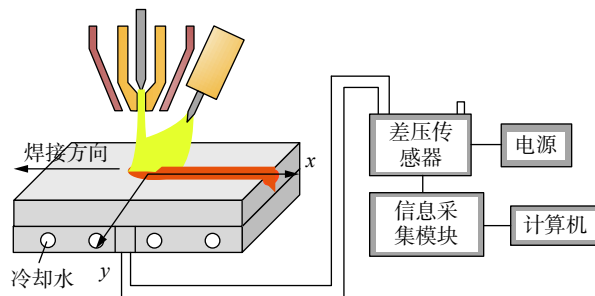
PAW-TIG 耦合电弧焊接装置示意图
